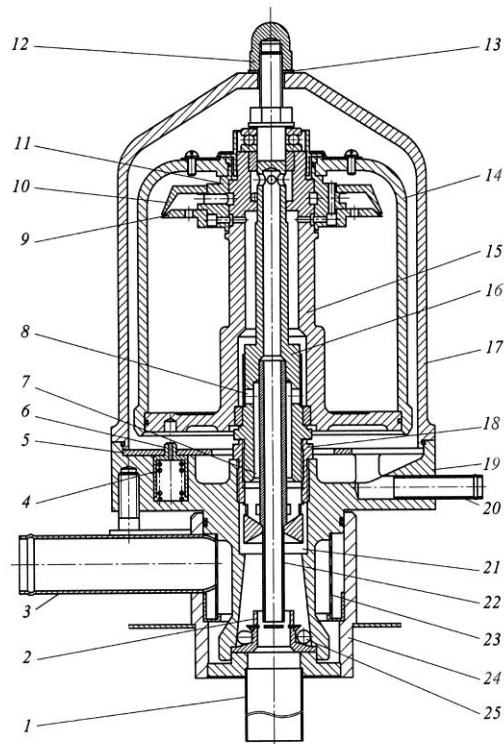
Комбинированный центробежный очиститель: 1 – сливной патрубков; 2 – сливной насадок; 3 – входной патрубков; 4 – пружина сухарика; 5 – пластина; 6 – сухарик; 7 – приемный канал; 8 – направляющий аппарат; 9 – нижний диск; 10 – верхний диск; 11 – втулка; 12 – гайка; 13 – шайба; 14 – стакан ротора; 15 – колонка ротора; 16 – ось ротора; 17 – колпак; 18 – вставка; 19 – гидроциклон; 20 – дренажная трубка; 21 – кольцевое отверстие; 22 – сливная трубка; 23 – фильтр-сетка; 24 – корпус; 25 – входное отверстие
